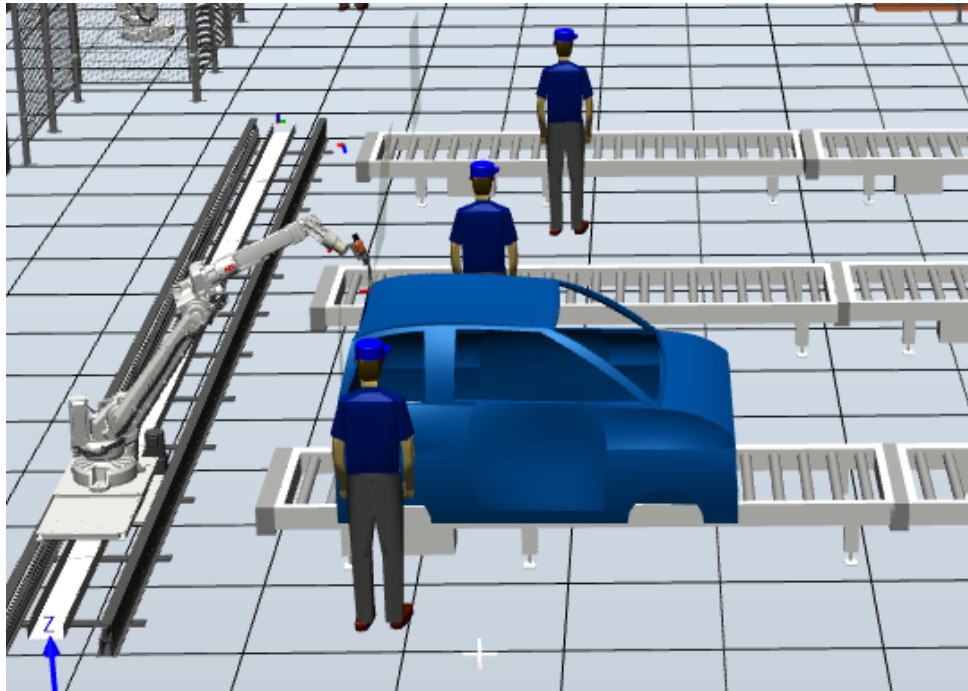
Soldadura de vehículo en el primer carril de la cuarta etapa.
